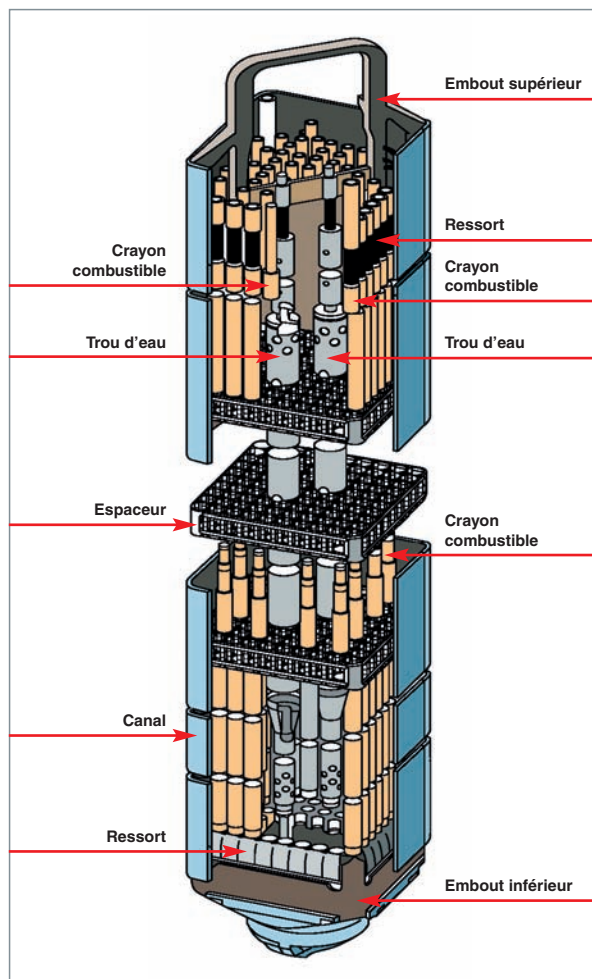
Assemblage combustible pour réacteur à eau bouillante.
